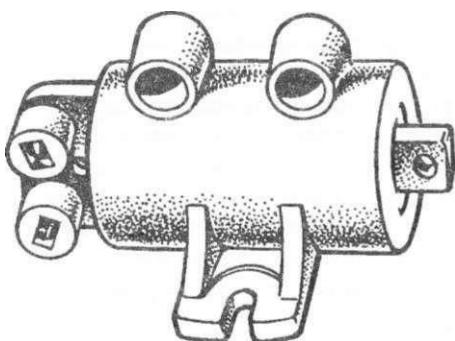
Загальний вигляд котушки запалювання 29.3 705
